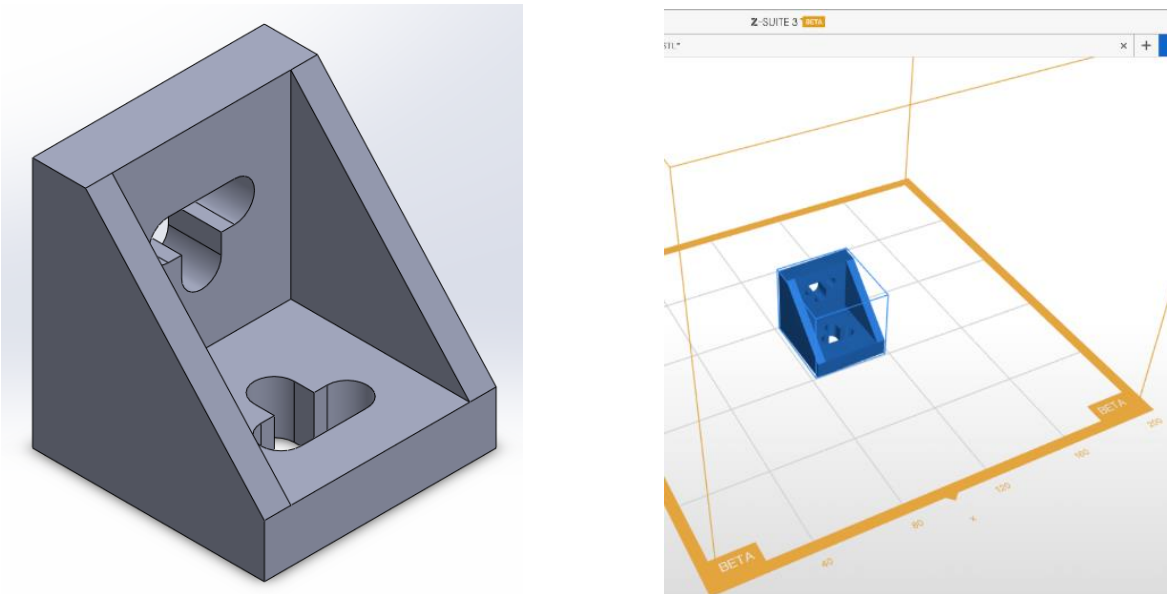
a) Pieza a imprimir, aún en SolidWorks. b) Pieza a imprimir en Z - Suite.
